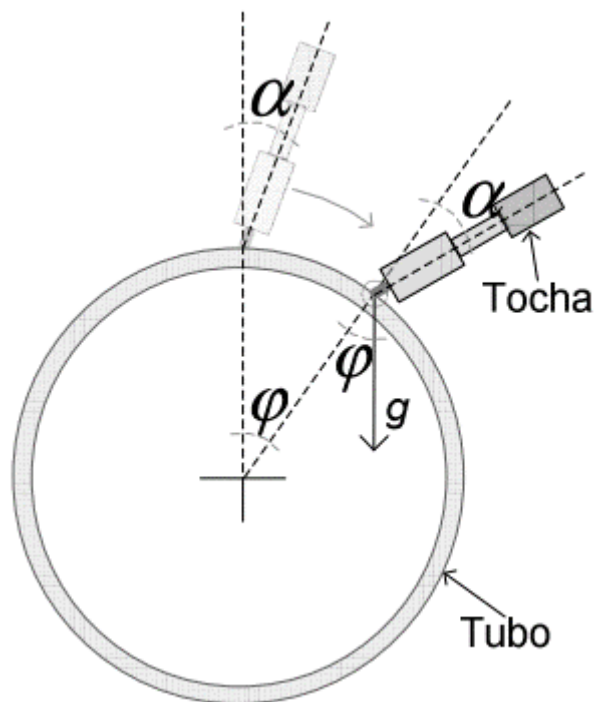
Ângulo de ataque α e ângulo de posição de soldagem φ . [7]
